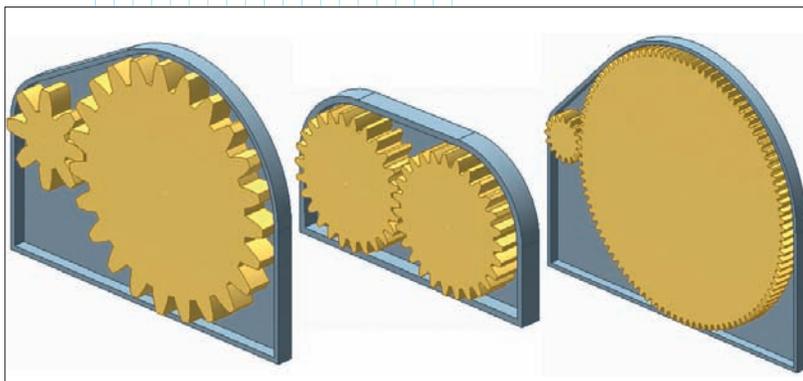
Варианты конфигурации конструкции корпуса редуктора для различных параметров зубчатой передачи в проекте Autodesk Inventor
